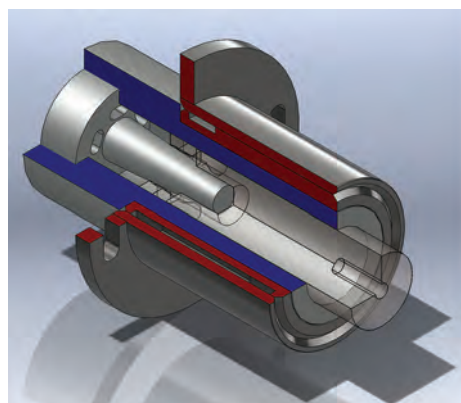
Трехмерная модель кристаллизатора для непрерывного литья трубных заготовок
